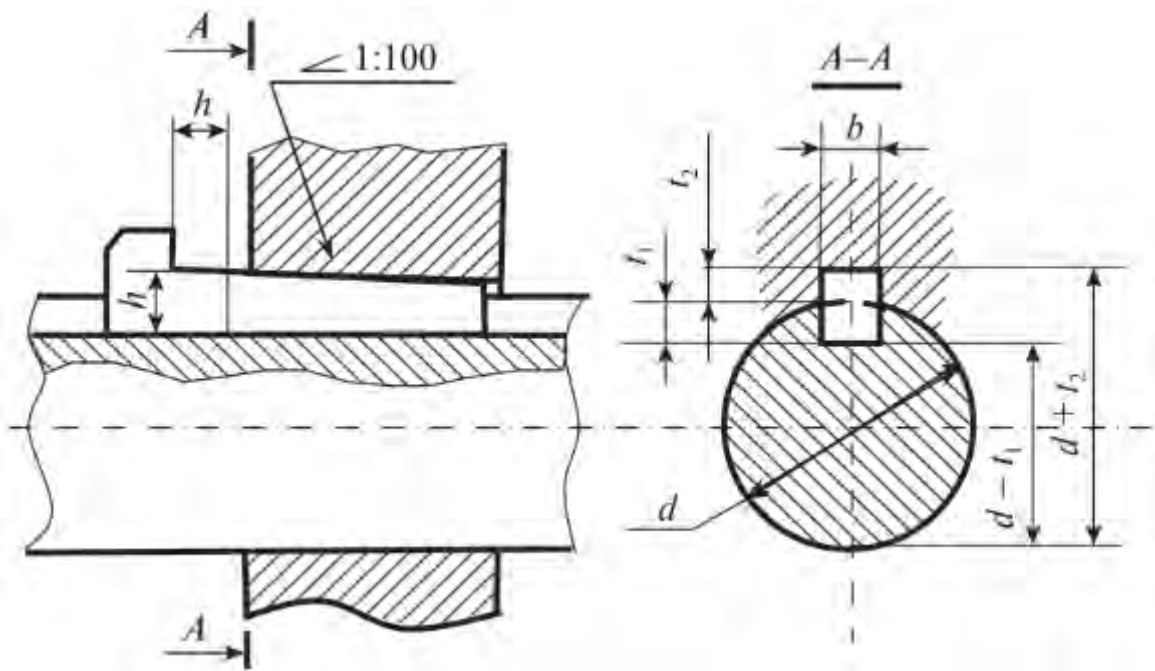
Схема шпоночного соединения с клиновой шпонкой
